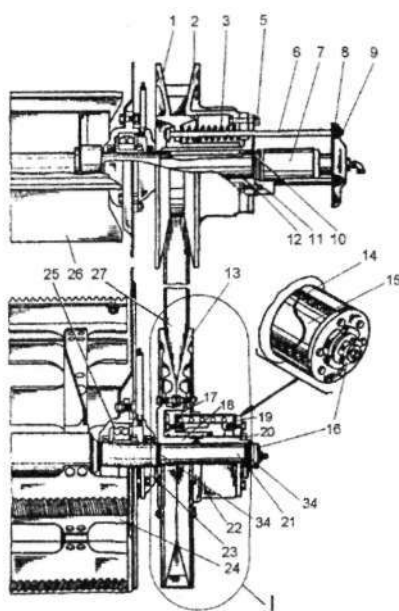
Вариатор молотильного барабана: 1 – диск подвижный ведущего шкива; 2 – диск неподвижный; 3 – пружина; 5, 6 – болты специальные; 7 – гидроцилиндр; 8 – фланец; 9, 20 – гайка; 10 – шайба стопорная; 11 – болт; 12 – вал битера; 13 – диск ведомого шкива; 14 – пружина; 15 – муфта; 16 – гайка; 17 – ступица неподвижная; 18 – ступица подвижная; 19 – крышка; 21 – вал барабана; 22 – кожух; 23 – опора вала; 24 – барабан молотильный; 25 – подшипник опорный; 26 – битер отбойный; 27 – ремень
